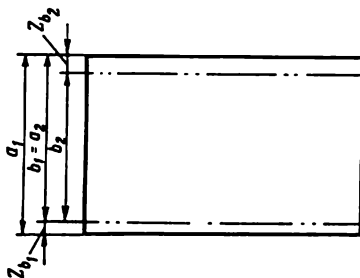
Surépaisseurs d'usinage asymétriques des surfaces extérieures
